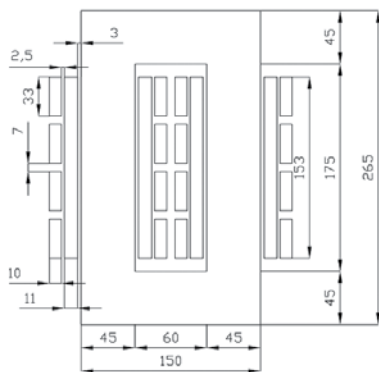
Corte y dimensiones principales en milímetros del transformador de prueba. Ancho del núcleo, 90 mm
